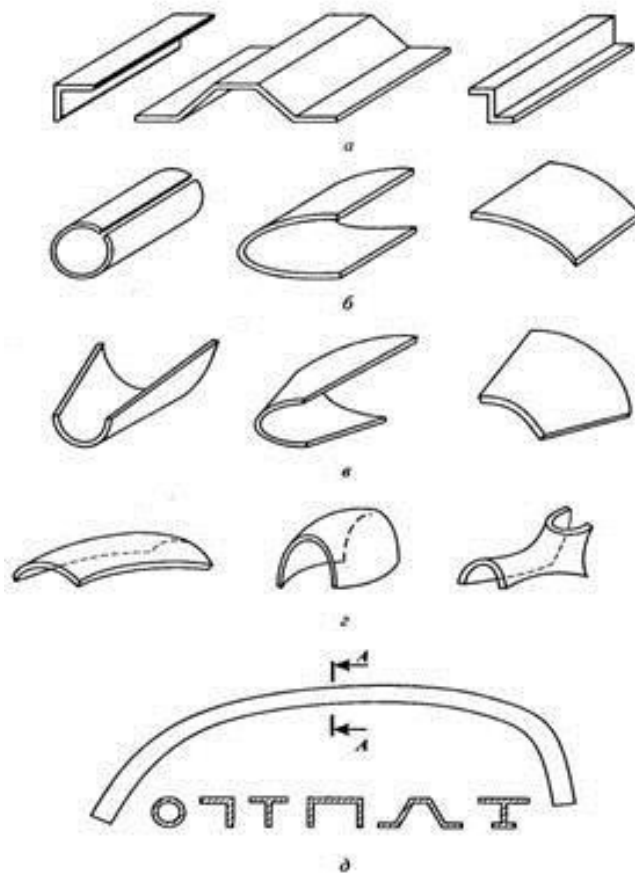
Типовые тонкостенные детали из листов и профилей: а - угловые детали из листового металла с прямолинейной образующей; б - цилиндрические детали из листового металла; в - конические детали из листового металла; г - выпуклые и выпукло-вогнутые детали из листового металла; д - криволинейные детали из профилей и труб
